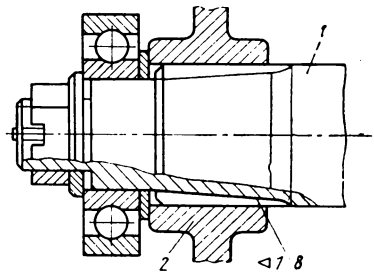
Шлицевое соединение с конической центрирующей поверхностью
